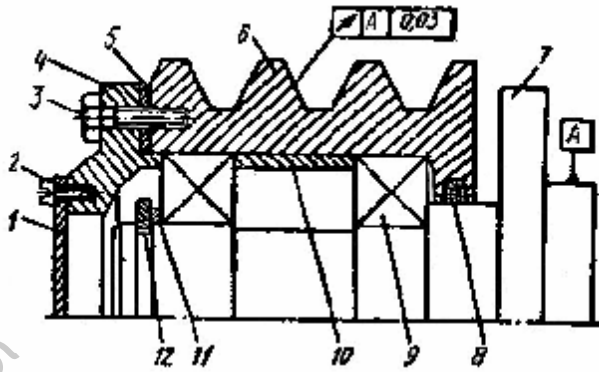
Эскиз ступицы в сборе: 1— крышка; 2,3— винты; 4— фланец; 5— прокладка; 6— шкив; 7— ступица; 8— кольцо уплотнительное; 9— подшипник; 10— втулка; 11— кольцо компенсационное; 12— кольцо стопорное
